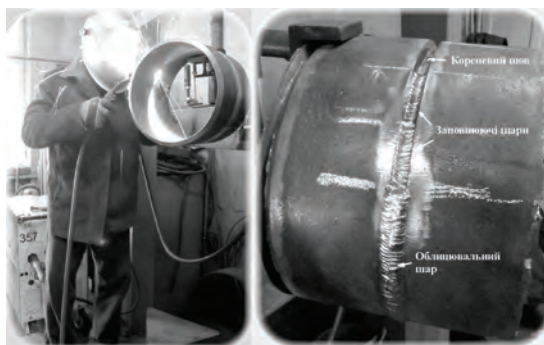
Механізоване зварювання неповоротного кільцевого стикового з'єднання
